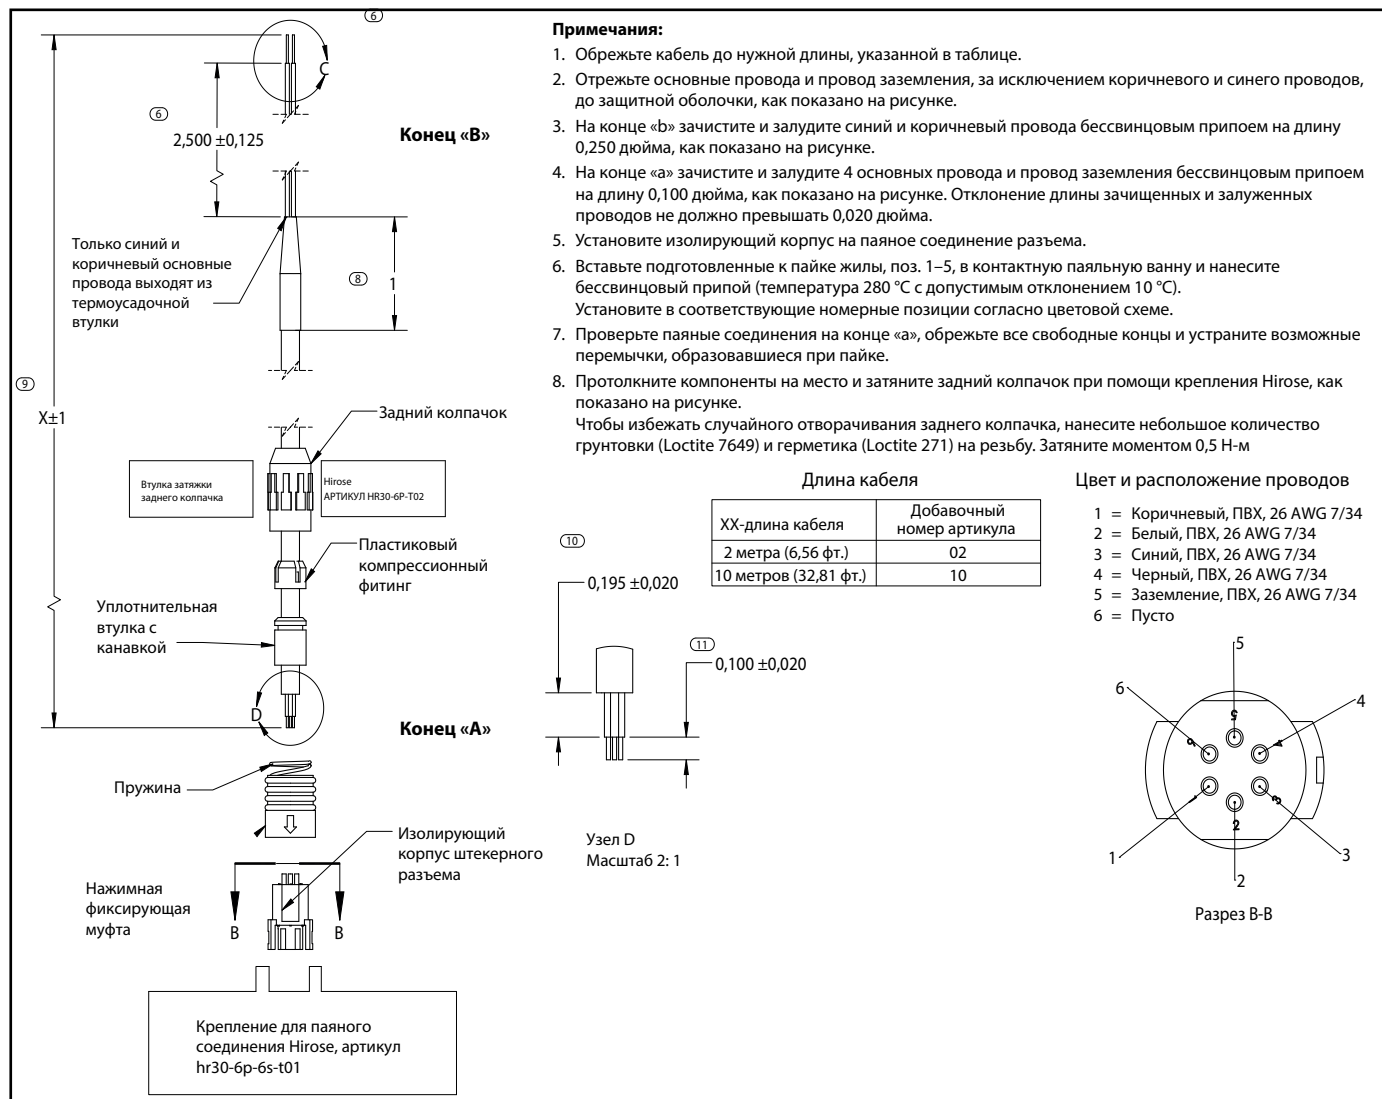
Кабель, стандартный (№ чертежа 704-1317, лист 2 из 2)
